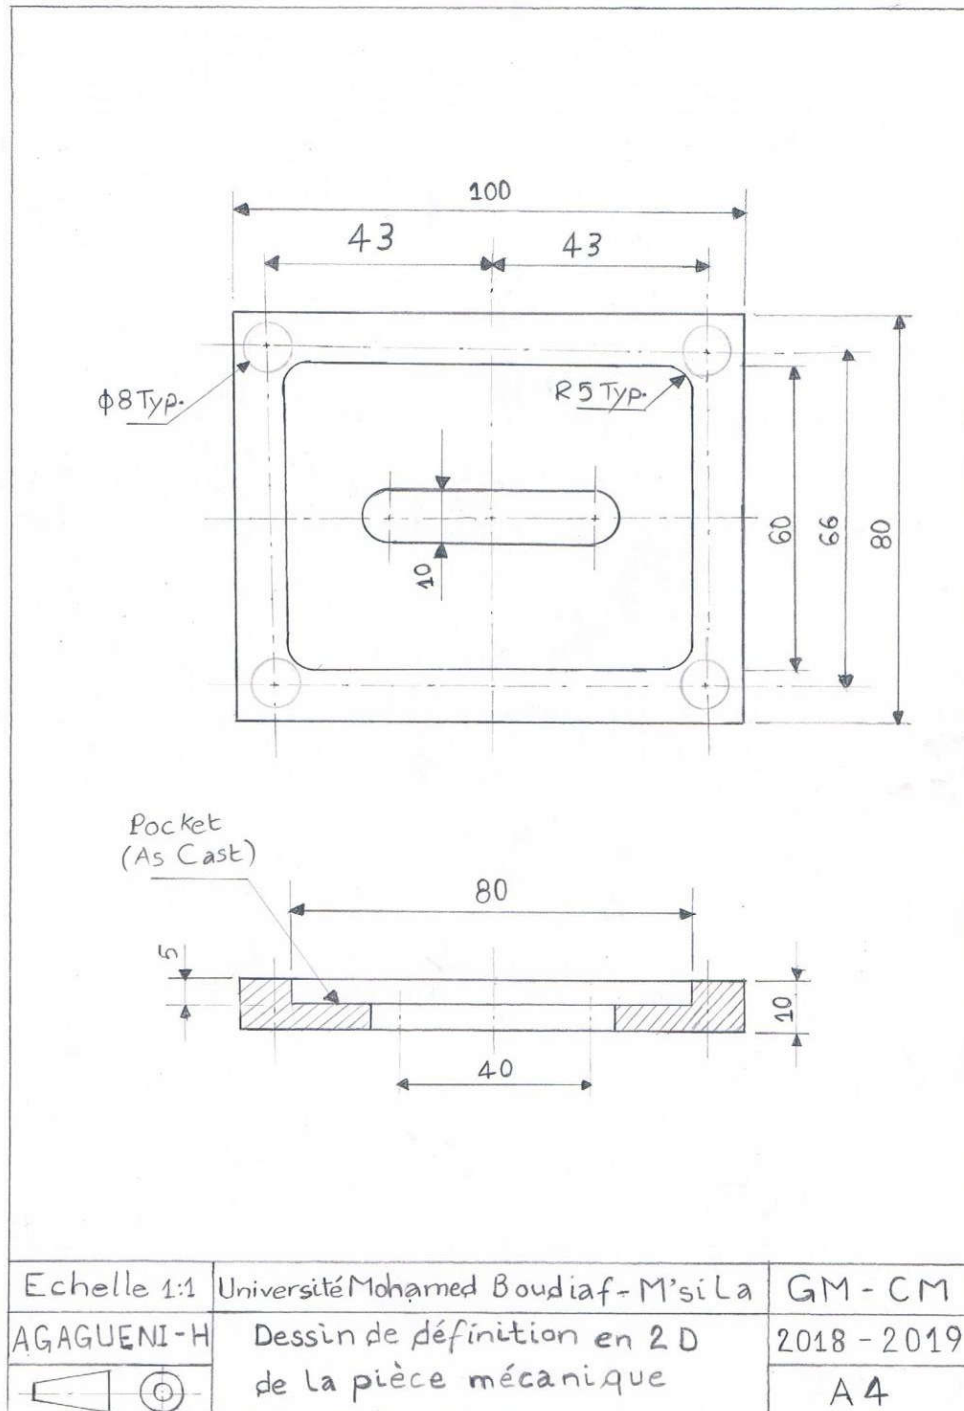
Dessin de définition en 2D de la pièce prismatique
